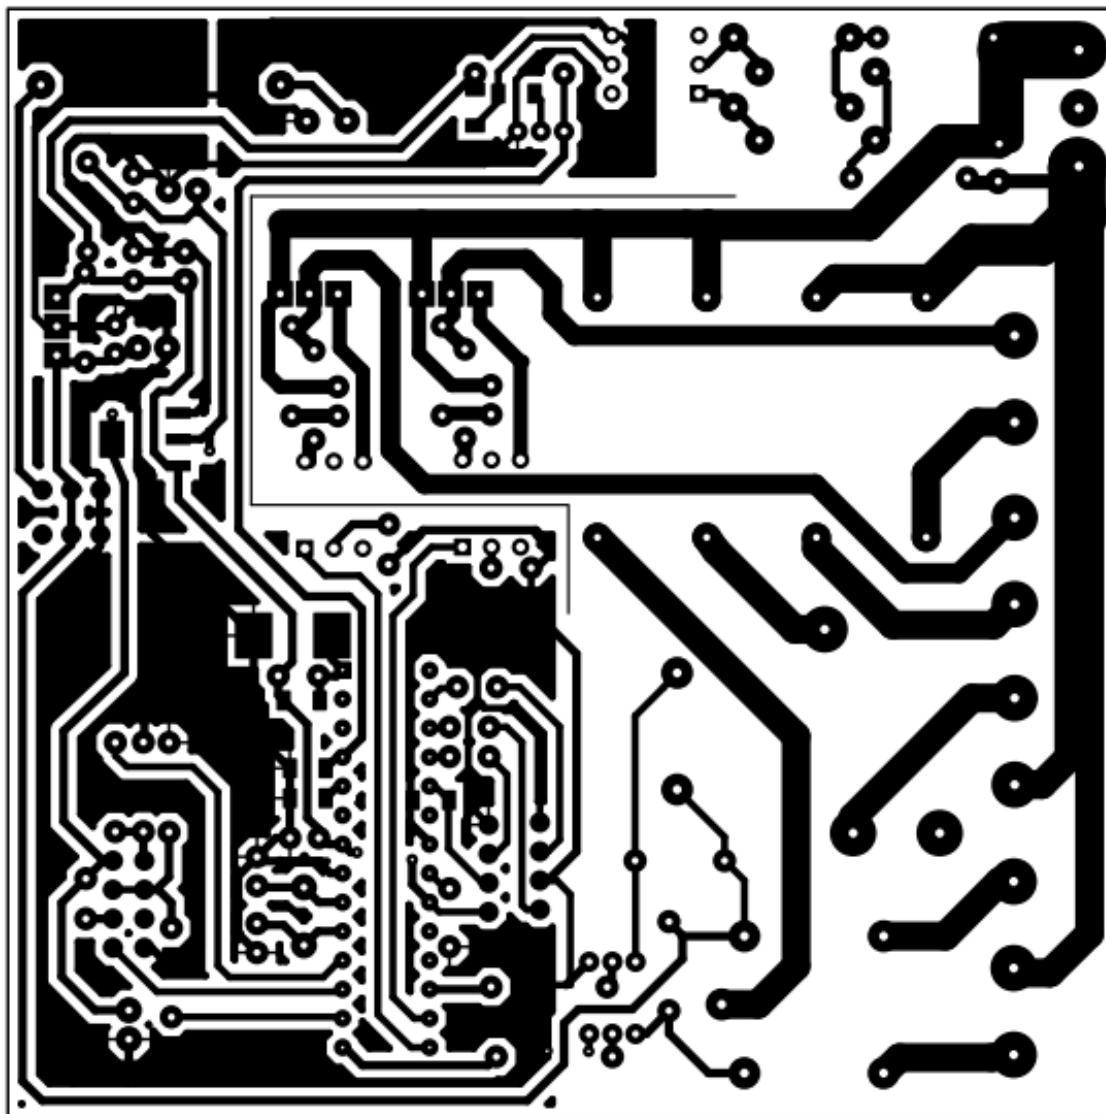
Plantilla PCB para el módulo de interruptores.
